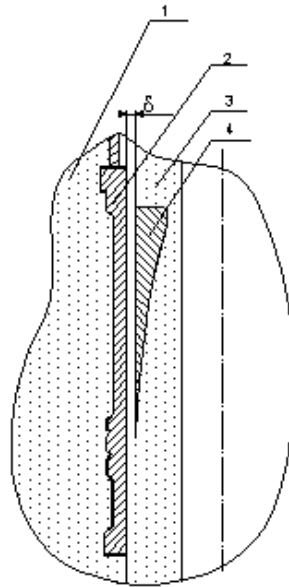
Схема отливки в песчано-глинистую форму втулки цилиндра судового дизеля с пассивным холодильником:
